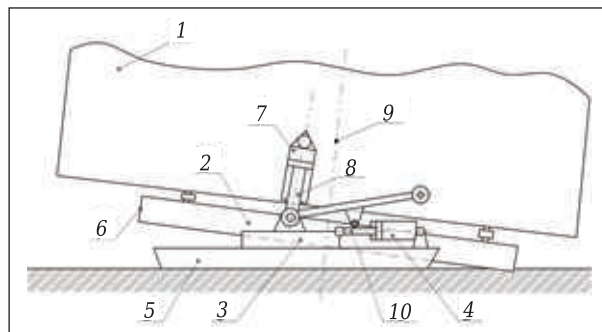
Трехопорный механизм шагания экскаватора-драглайна: 1 — корпус; 2 — база; 3 — скользящий элемент; 4 — тяговый гидроцилиндр; 5 — опорный башмак; 6 — передняя кромка базы; 7 — подъемный гидроцилиндр; 8 — шток подъемного гидроцилиндра; 9 — центр масс экскаватора-драглайна; 10 — шток тягового гидроцилиндра
